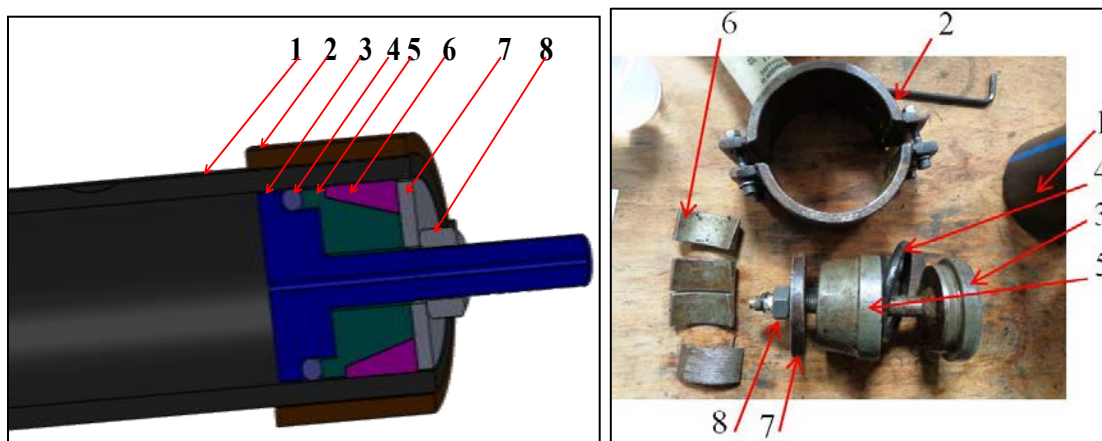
Composantes du bouchon de serrage; 1: Tube PE100; 2: bride; 3: mandrin; 4: joint torique; 5, 6: composantes de serrage; 7: bride; 8: écrou
